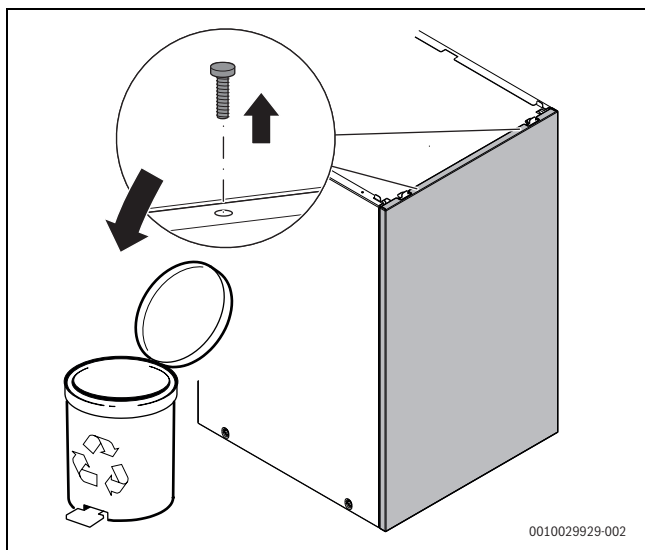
Снятие транспортного фиксатора в передней части облицовки бака-водонагревателя
